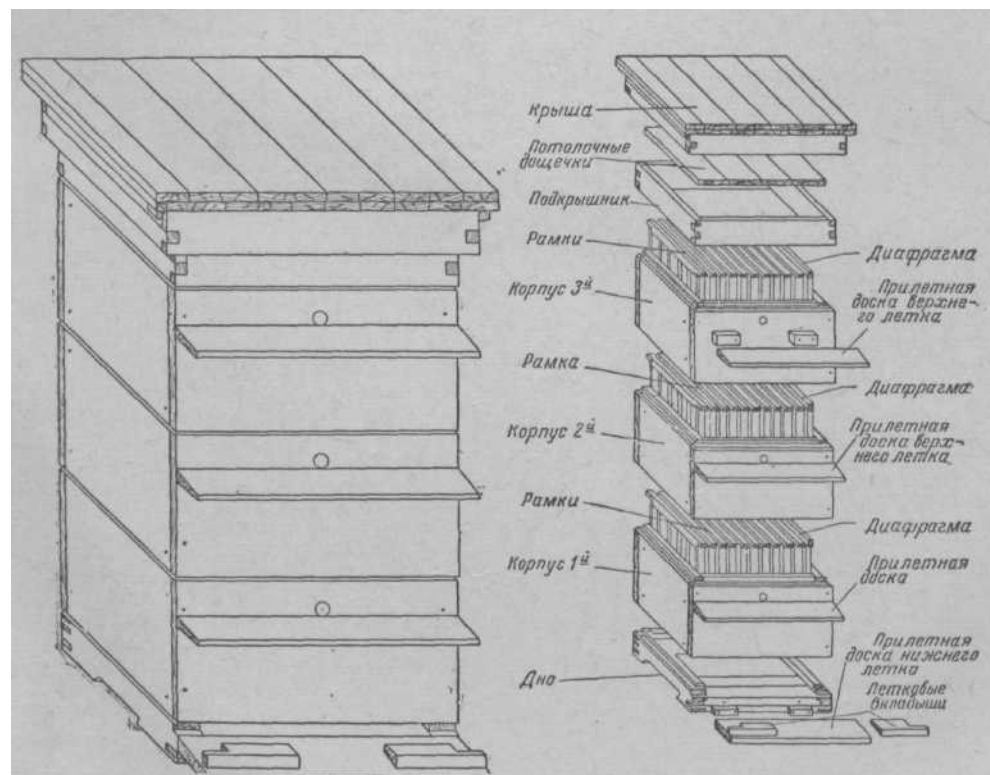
Одностенный многокорпусный улей (общий вид и детали устройства).
